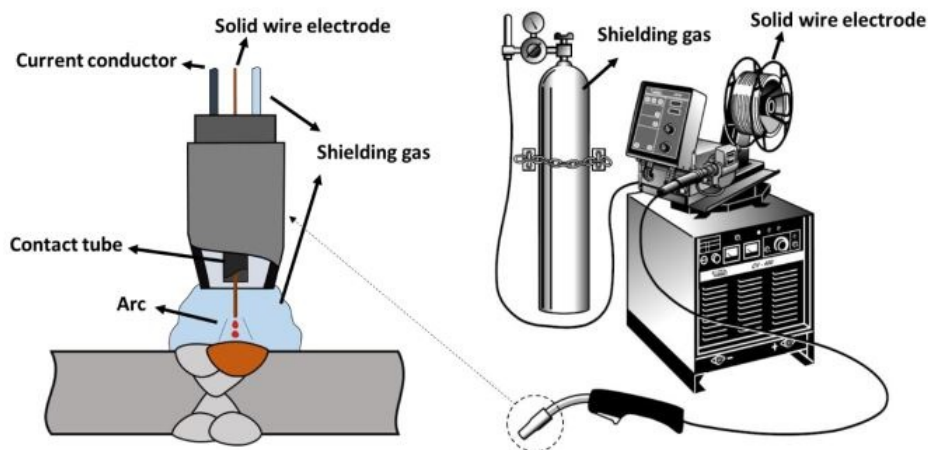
Illustration du procédé de soudage MIG-MAG [Akçay ,2015]
